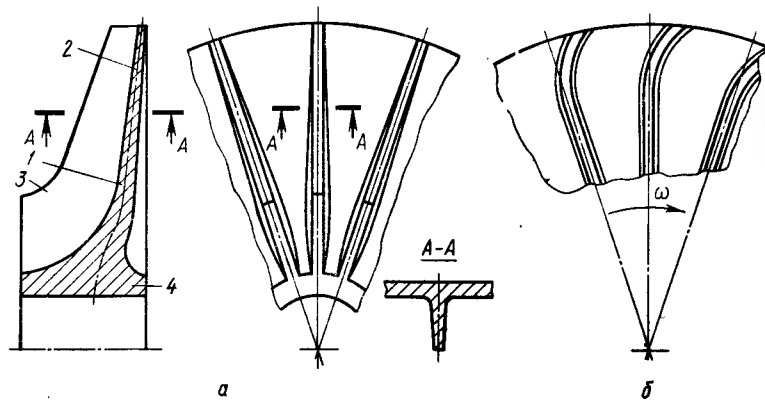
Конструктивные формы рабочего колеса центробежного компрессора (а) и элемент активного центробежного колеса с изгибом лопаток в сторону вращения (б):
